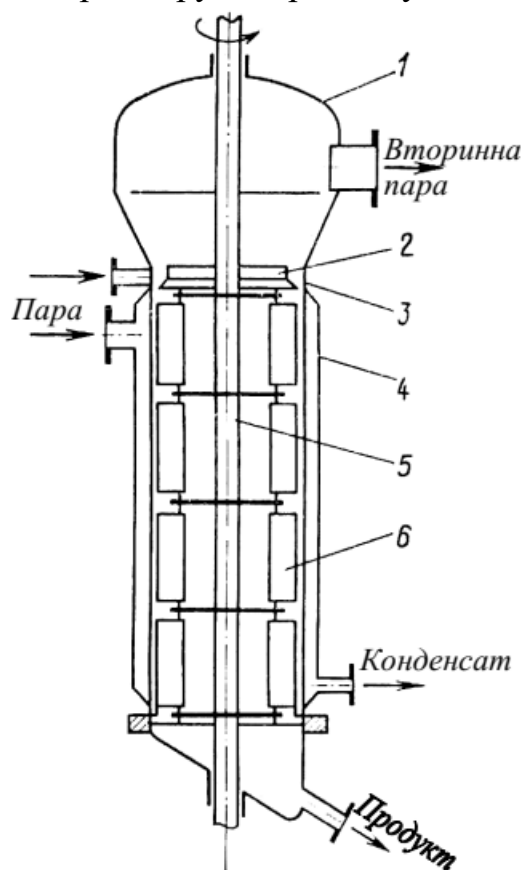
Роторно-плівковий випарний апарат: 1 – сепаратор; 2 – розподільний пристрій; 3 – нагрівальна камера; 4 – нагрівальна парова оболонка; 5 – ротор; 6 – лопаті
